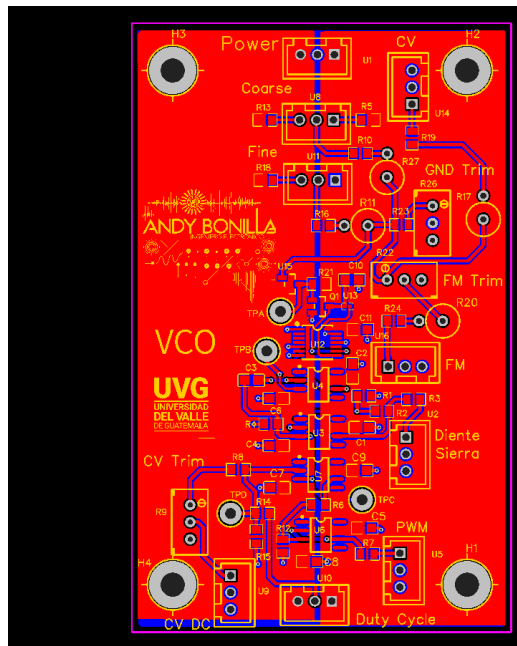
Vista 2D de PCB oscilador controlador por voltaje
